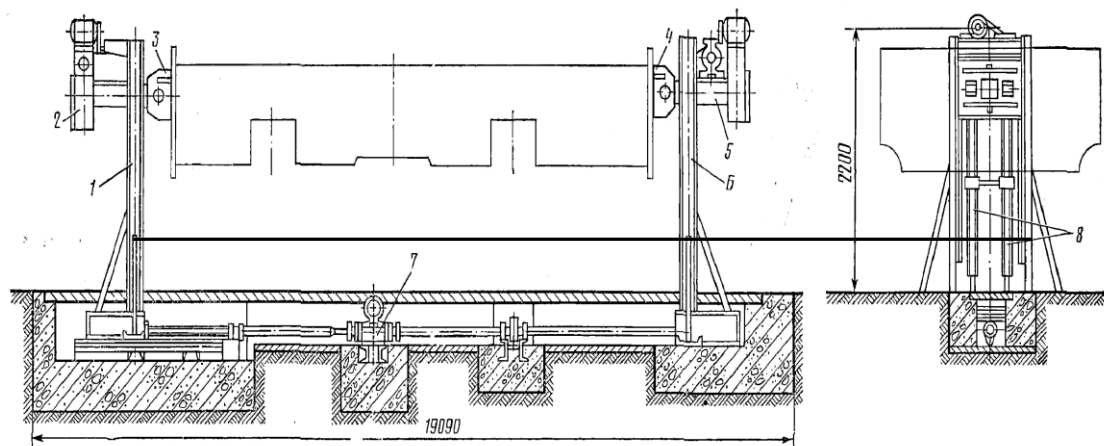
Двухстоечный кантователь для сварки рамы:
